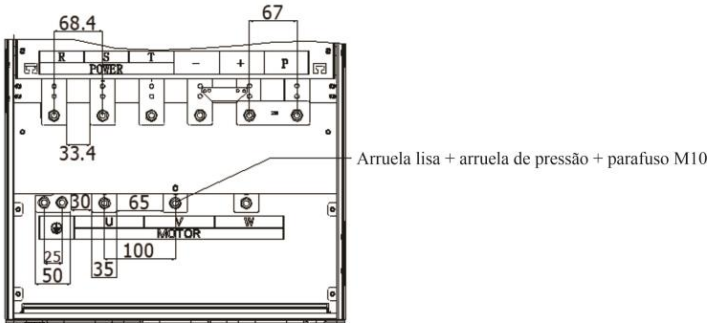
Terminal circuito principal 187~220kW G3/F3 (Chassis No.: A11)
